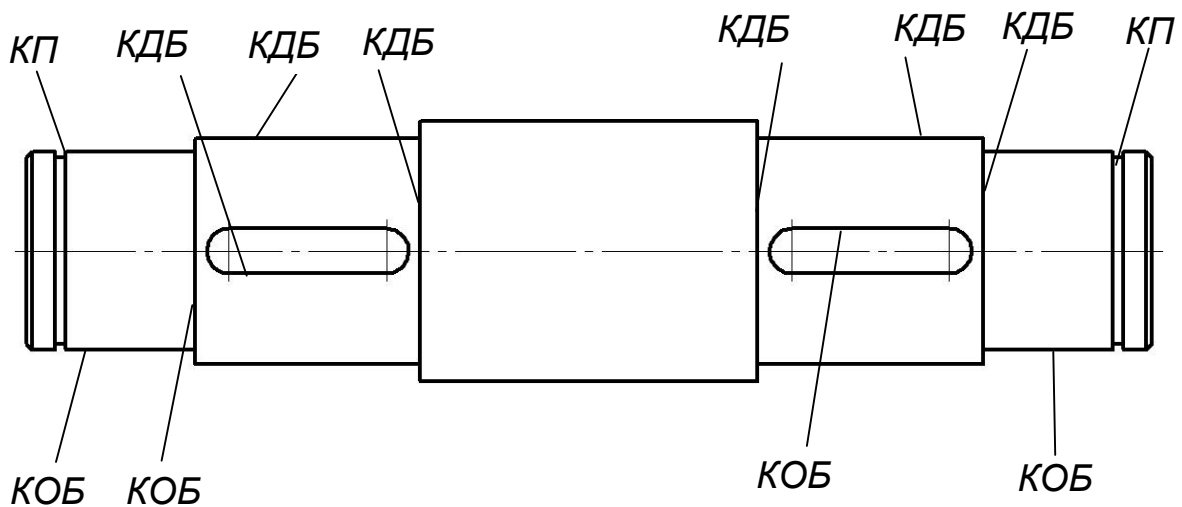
Функціональне призначення поверхонь проміжного вала: КОБ — конструкторська основна база, КДБ — конструкторська допоміжна база, КП — кріпильна поверхня
